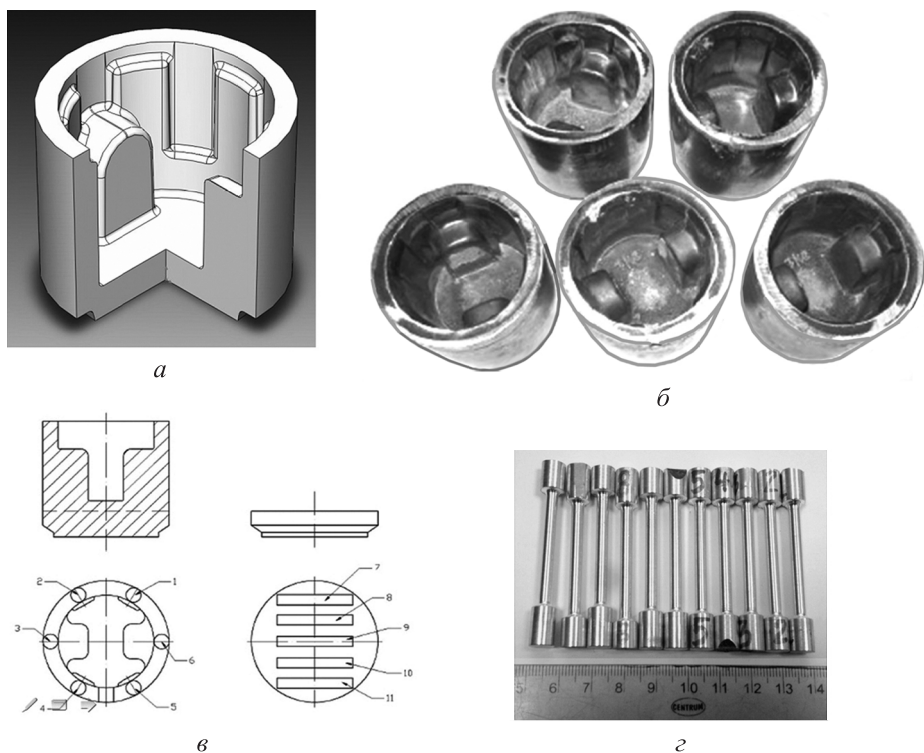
Общий вид модельной штампованной заготовки и схема вырезки образцов:
